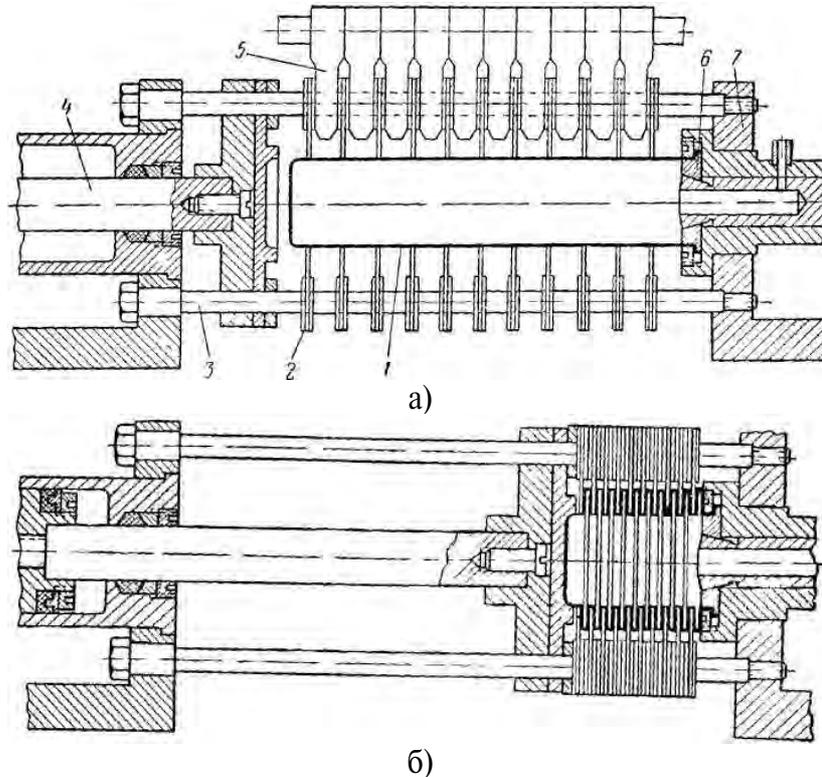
Устройство для гофрирования мехов гидравлическим способом:
